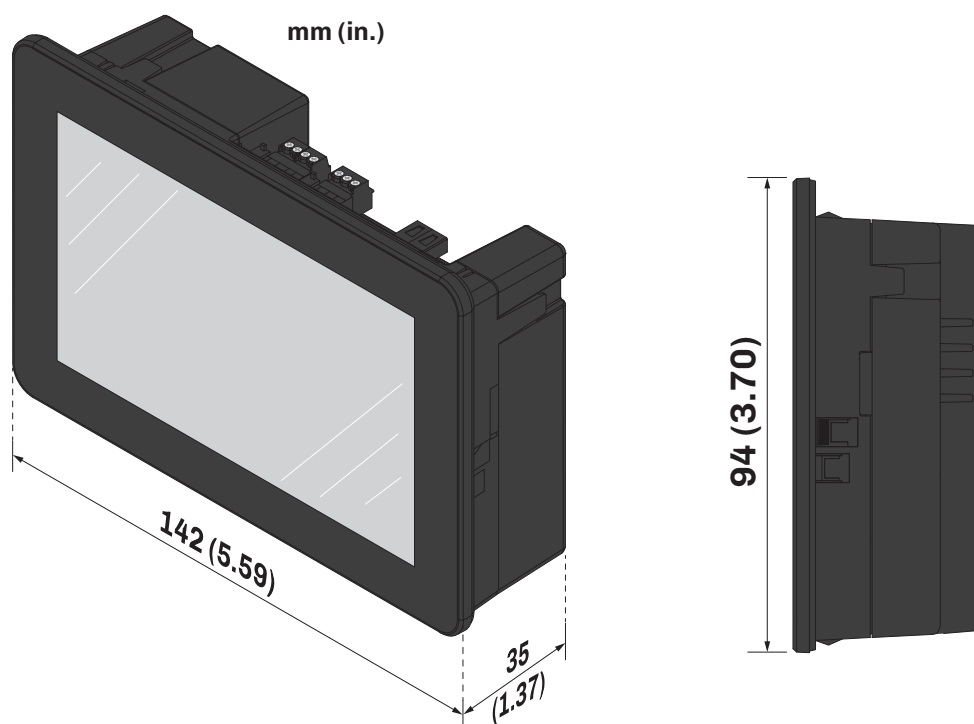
Dimensioni interfaccia utente Vcolor 739 M a montaggio con frontale sporgente
